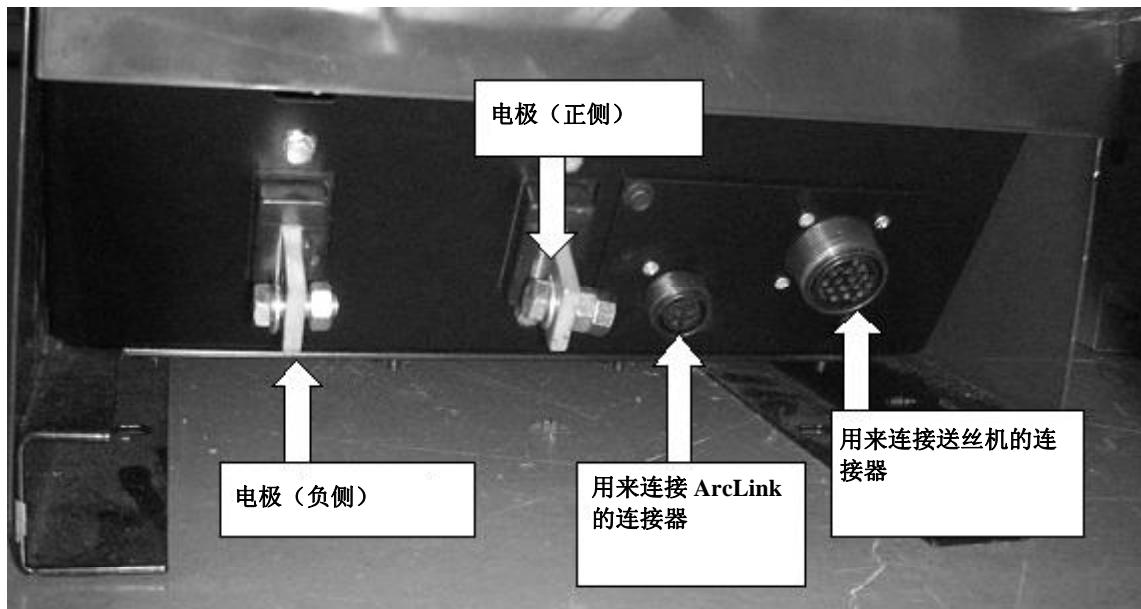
(d) ROBOWELD iC/E 用焊接电源装置 (CV350-R) 的连接接口
